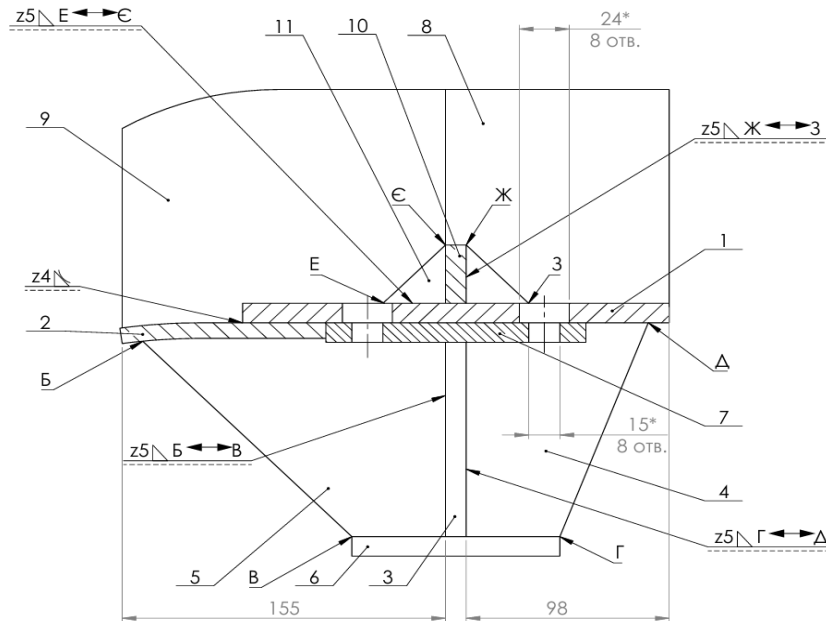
Поперечний переріз пластини модернізованого пластинчастого живильника: точки: Б, В, Г, Д, Ж, З, Е, Є – точки зварювання; 1 – основа; 2 – дугоподібний елемент; 3 – поздовжнє ребро; 4 – заднє поперечне ребро; 5 – переднє поперечне ребро; 6 – опорний елемент; 7 – з'єднувальний елемент; 8 – задній реборд; 9 – передній реборд; 10 – поздовжнє додаткове ребро; 11 – додаткове поперечне ребро
